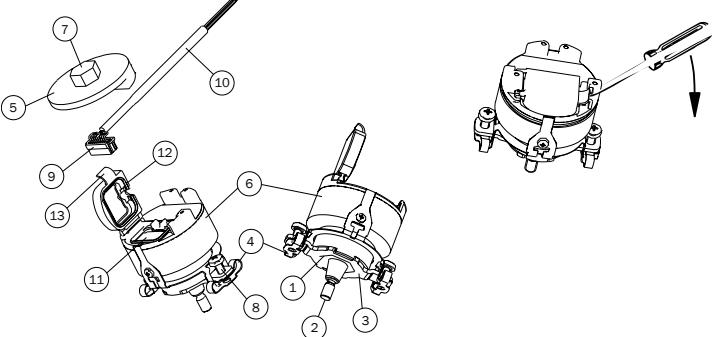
Disegno di assemblaggio SKS36S/SKM36S albero conico
